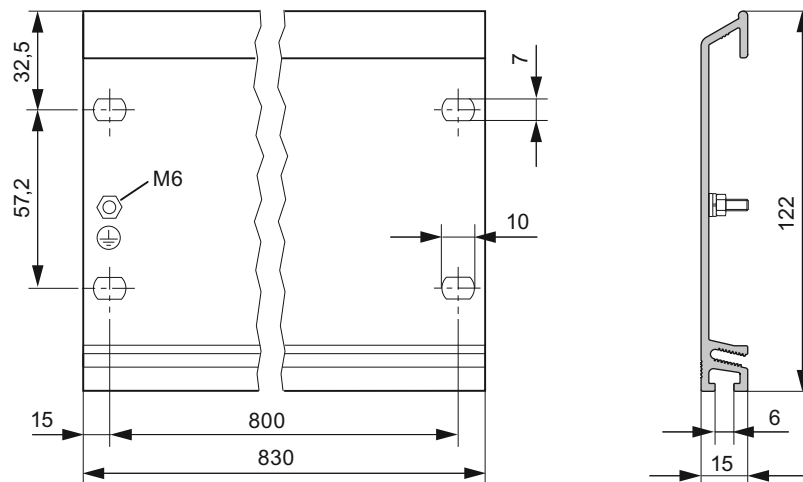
Croquis acotado del perfil soporte en ancho estándar de 830 mm
